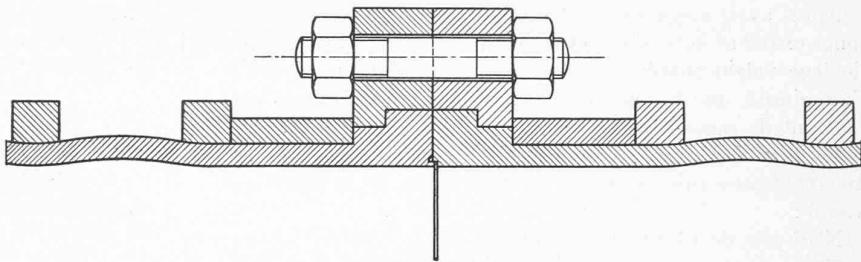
Joint d'une conduite en tuyaux multiondes frettés.
